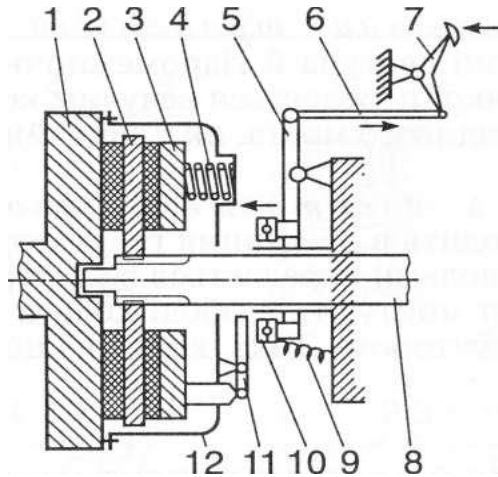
Кінематична схема сухого однодискового фрикційного зчеплення (1- маховик двигуна; 2- ведений диск зчеплення; 3- натискний диск; 4- пружина; 5- важіль зчеплення; 6- тяга; 7- педаль зчеплення; 8- первинний вал коробки передач; 9- пружина відтискна; 10- підшипник вижимний; 11- важіль відтискний; 12- кожух зчеплення).
